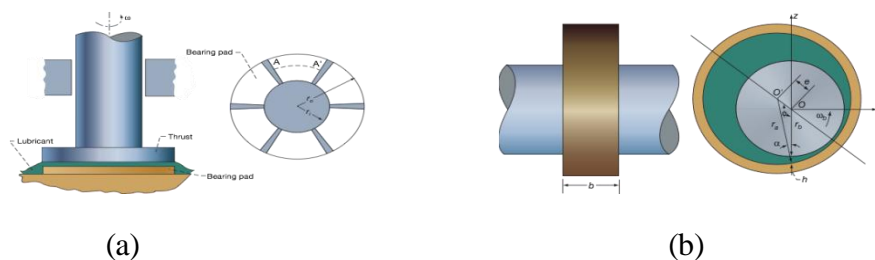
Konstruksi *bearing* (a) *slider bearing* (b) *roller bearing* [23]
